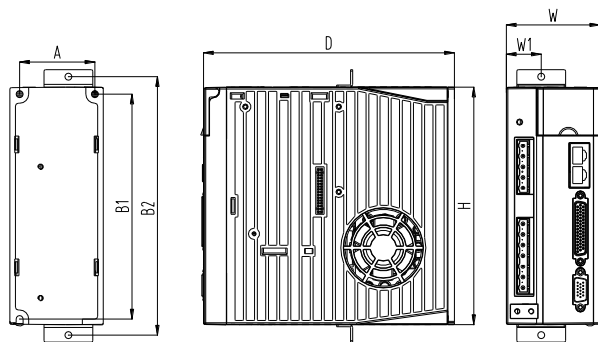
Габаритные размеры приводов типоразмеров А, В, С, D
